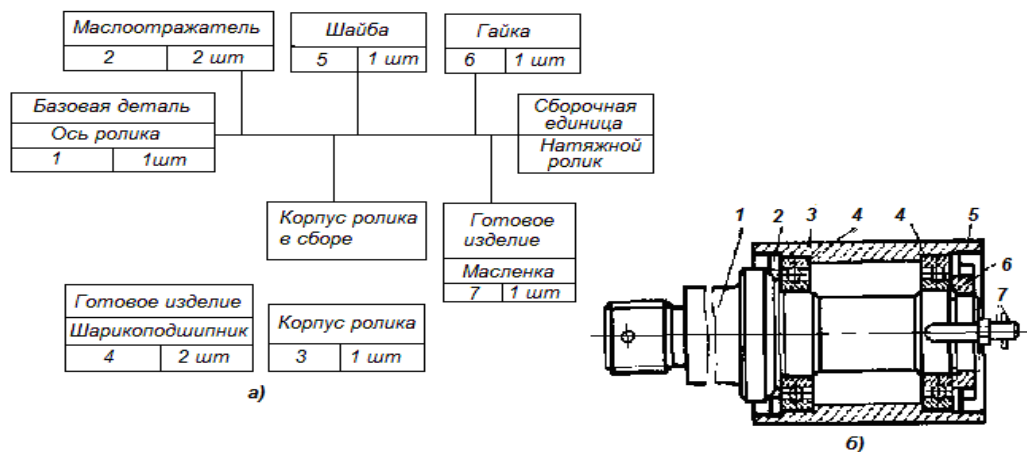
Схема сборки (а) сборочной единицы (б)
